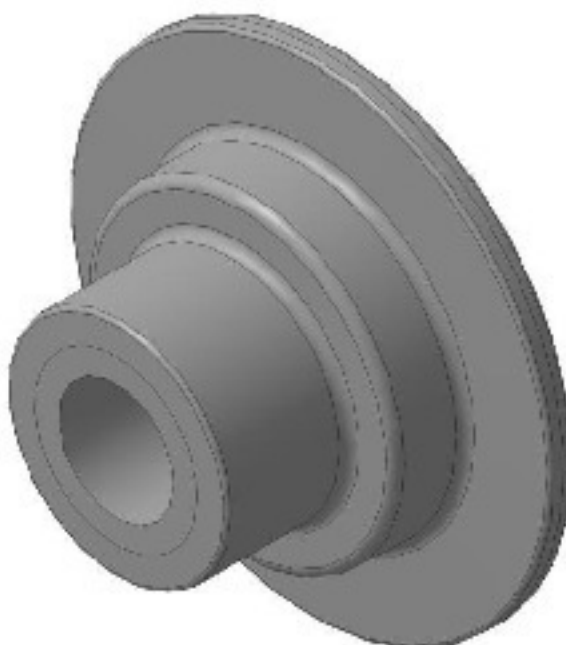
3D-модель заготовки виготовленої штампуванням на ГвП
